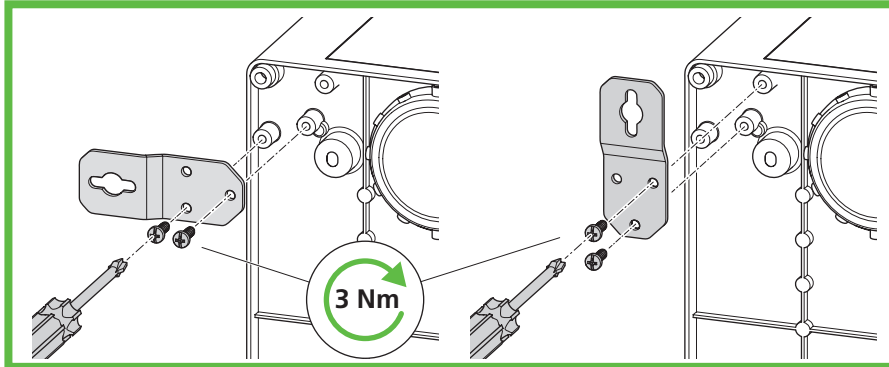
Montage Außenbefestigungsflasche ABL-10/ES
